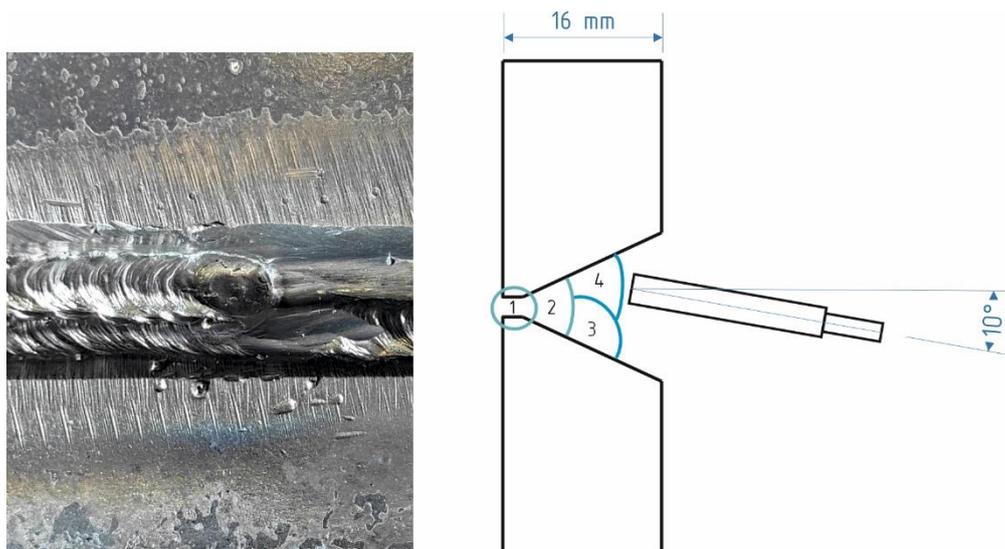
Сварка горизонтальных швов, проходы 1-4
